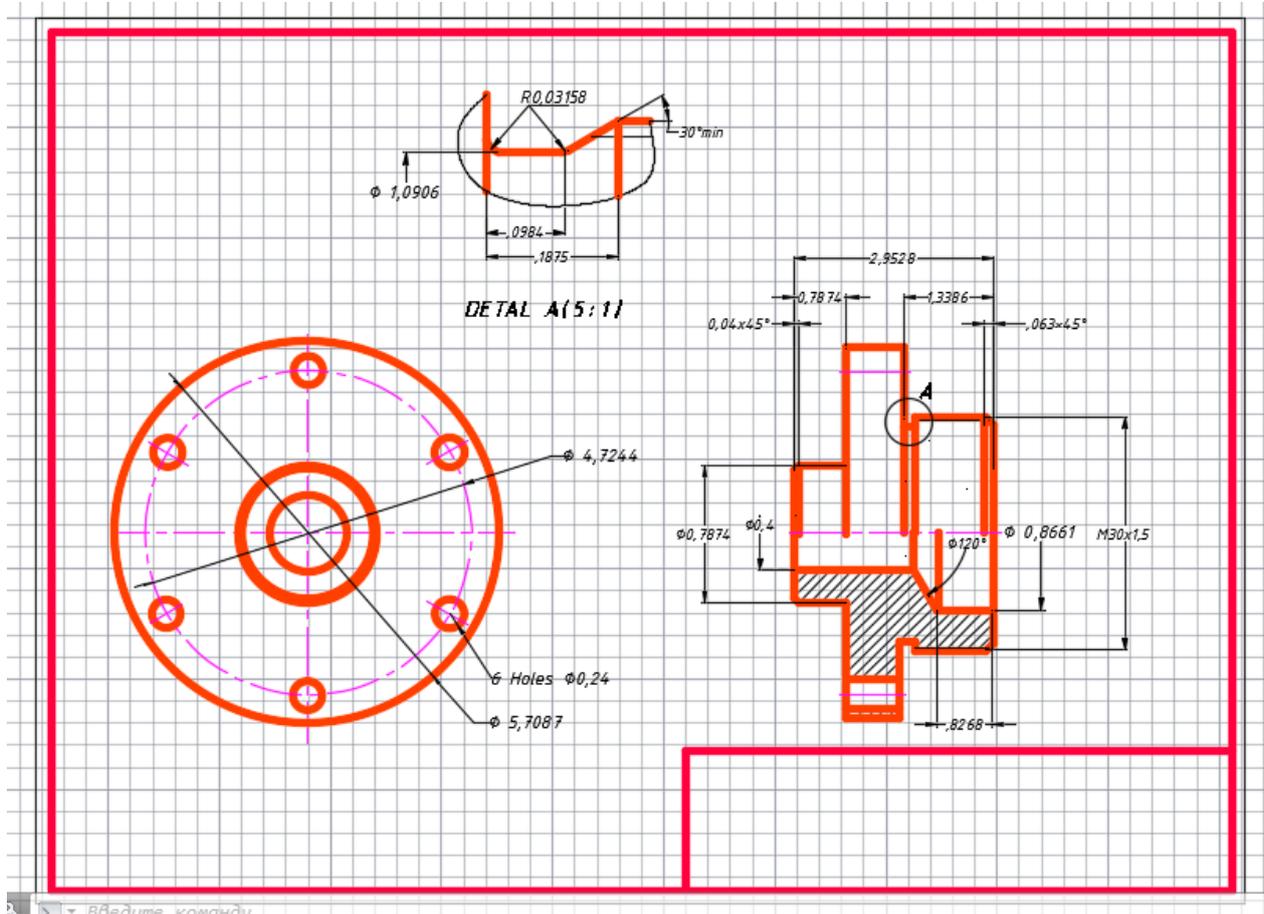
Рабочий чертеж крышки по стандартам ANSI
